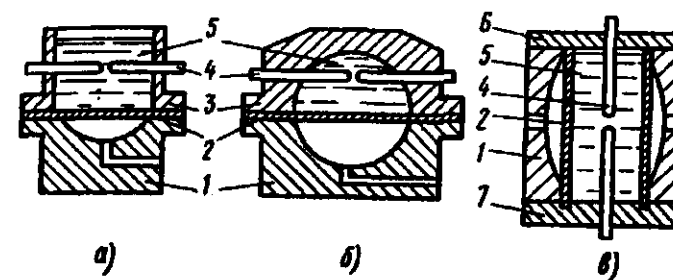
Схемы электрогидравлической штамповки: а — плоской заготовки в открытой емкости; б — плоской заготовки в замкнутой емкости; в — трубчатой заготовки в замкнутой емкости; 1 — матрица; 2 — заготовка; 3 — емкость; 4 — электрод; 5 — вода; 6, 7 — верхняя и нижняя крышки
